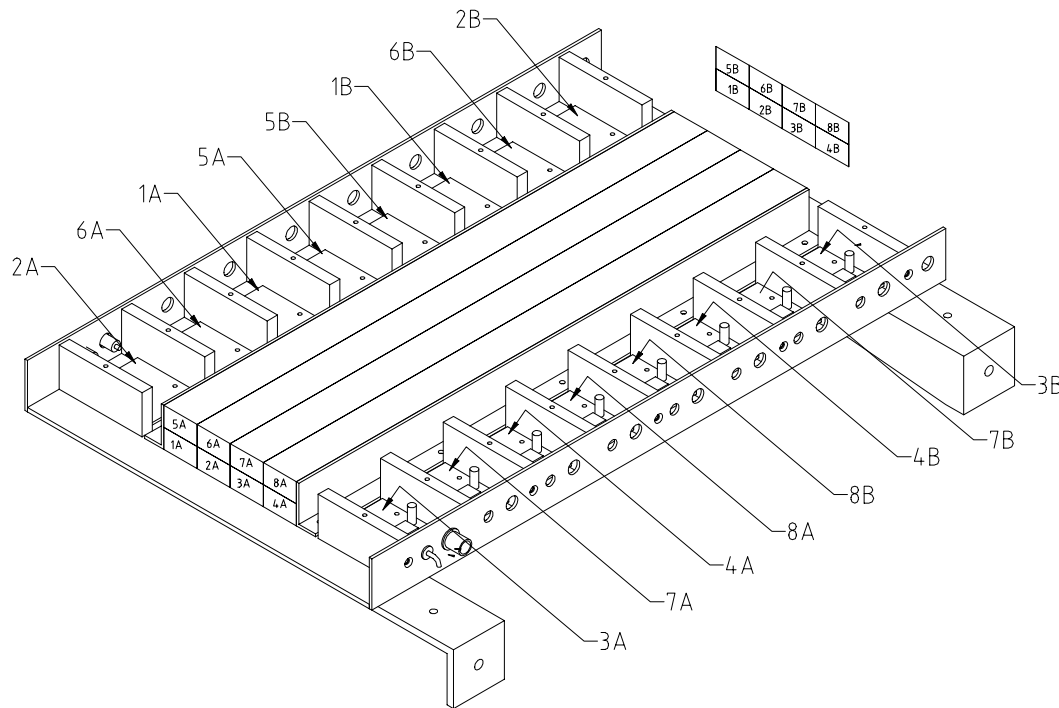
Schema della disposizione delle barre all'interno della struttura metallica di contenimento.
